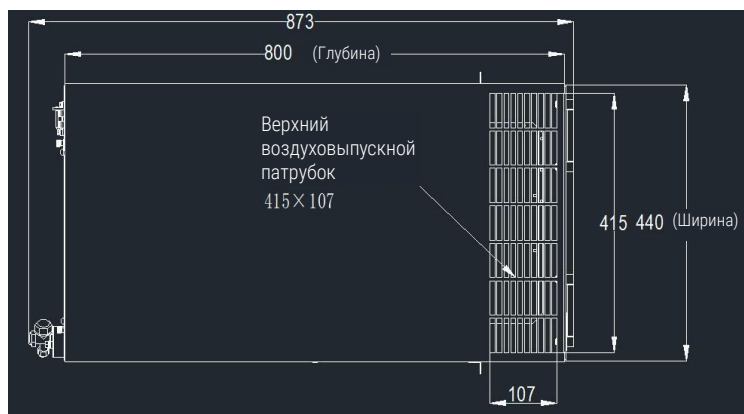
Чертеж габаритных размеров внутреннего блока мощностью 3,7 кВт
